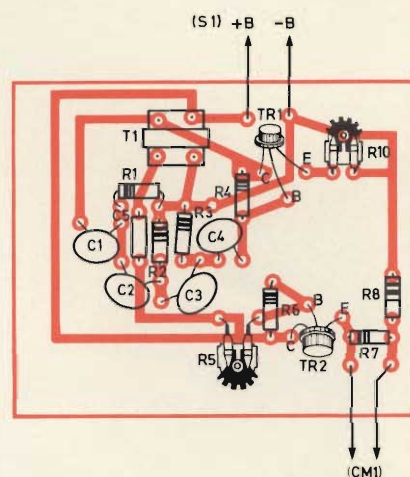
Circuito stampato e cablaggio dei componenti dello schema di figura 1.
